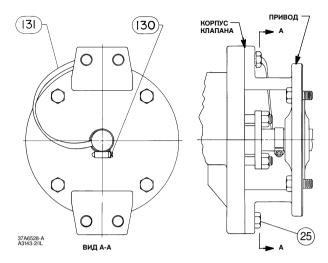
Дополнительный кабель заземления для корпуса в сборе с валом
